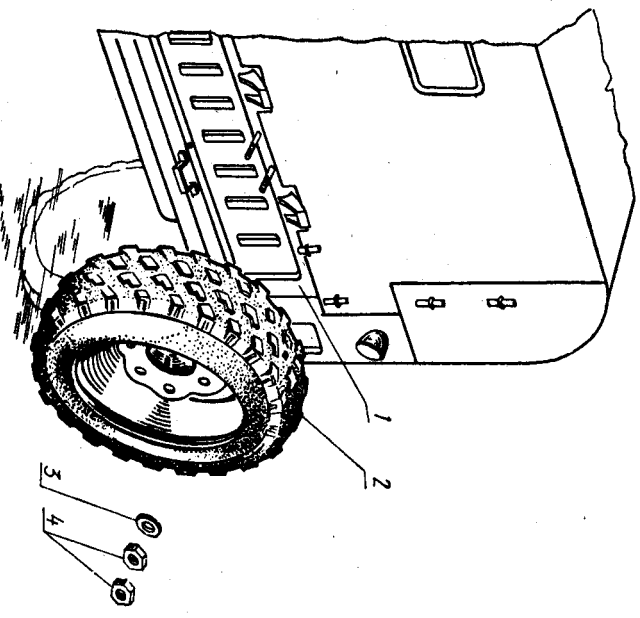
Крепление запасного колеса: 1 — задний борт автомобиля; 2 — колесо с шиной в сборе; 3 — шайба; 4 — гайка.
